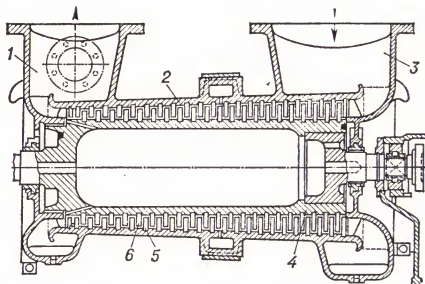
Осевого компрессор: 1 — канал для подачи сжатого газа; 2 — корпус; 3 — канал для всасывания газа; 4 — ротор; 5 — направляющие лопатки; 6 — рабочие лопатки.
